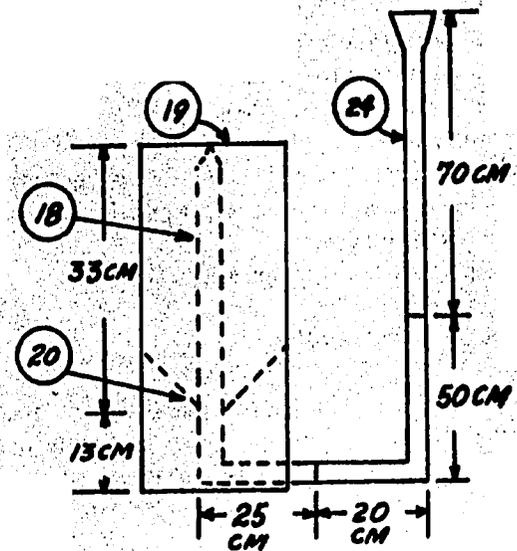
DETALLE DE LA PIEZA 19, TOLVA, Y DE LA PIEZA 24, TUBO. LAS LINEAS DISCONTINUAS INDICAN LA PIEZA 18, Y LA PIEZA 20, TUBO.
